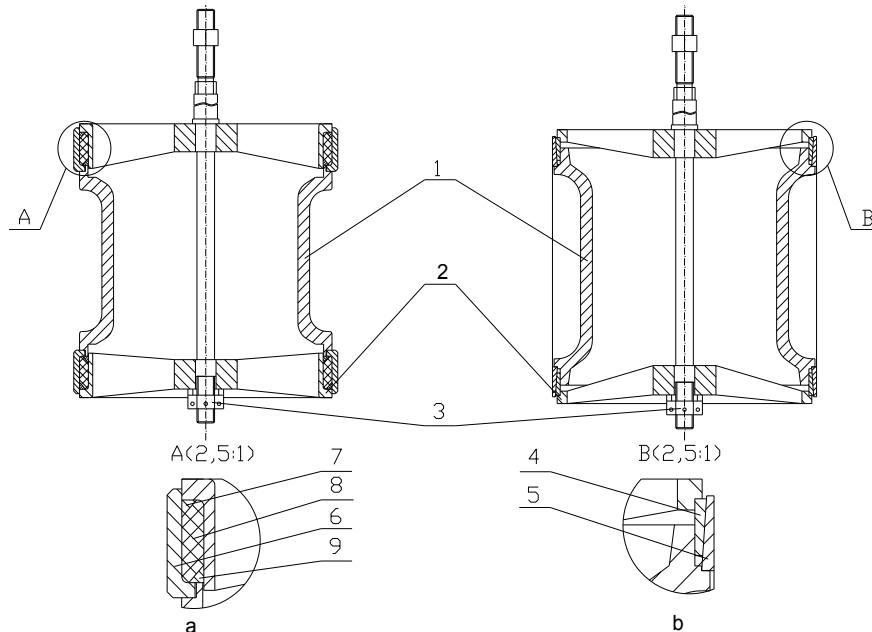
Золотник управления паровоздушным молотом: а – с цилиндрическими втулками; б – с коническими втулками
